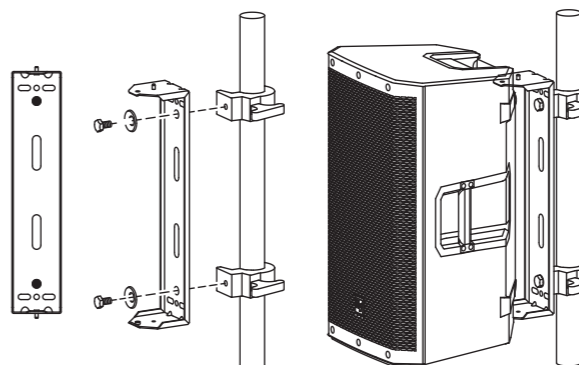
Vertikale Montage mit TCA-1 Traversenklemmen
